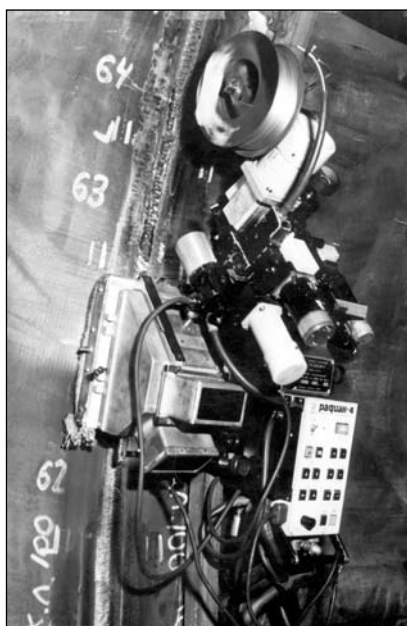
Сварочный автомат «Радиян-4» с адаптивным управлением
